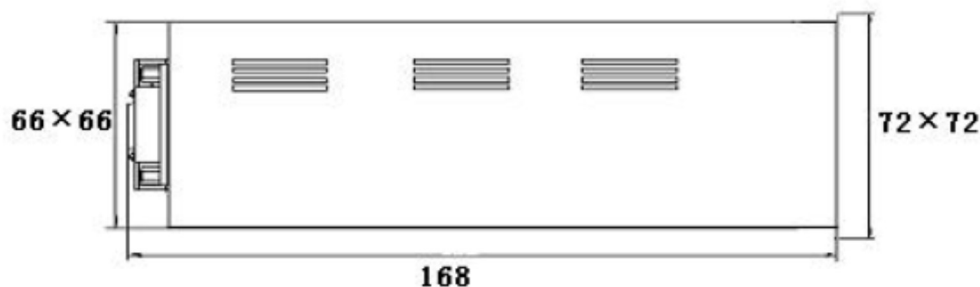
Габаритные размеры корпуса контроллеров D08-1G
